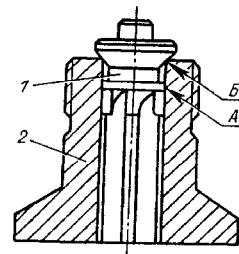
Клапан 4 нагнетательный /рис. 55/
